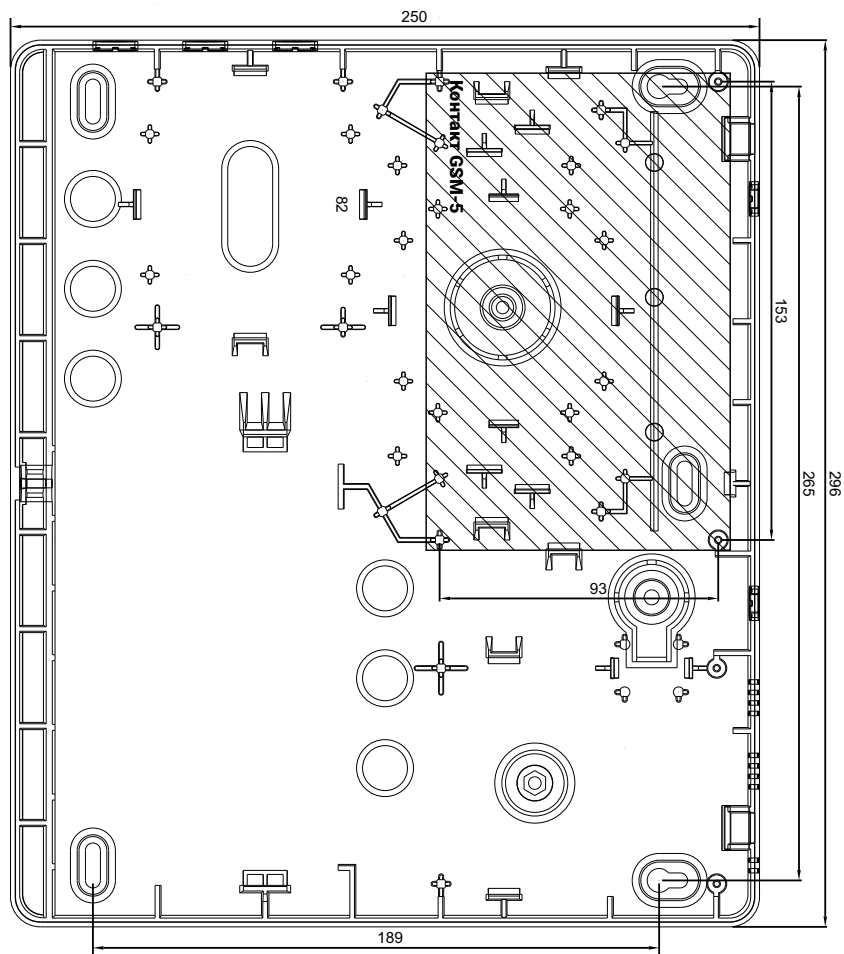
Установка панели в корпус «Контакт» 7 Ач
